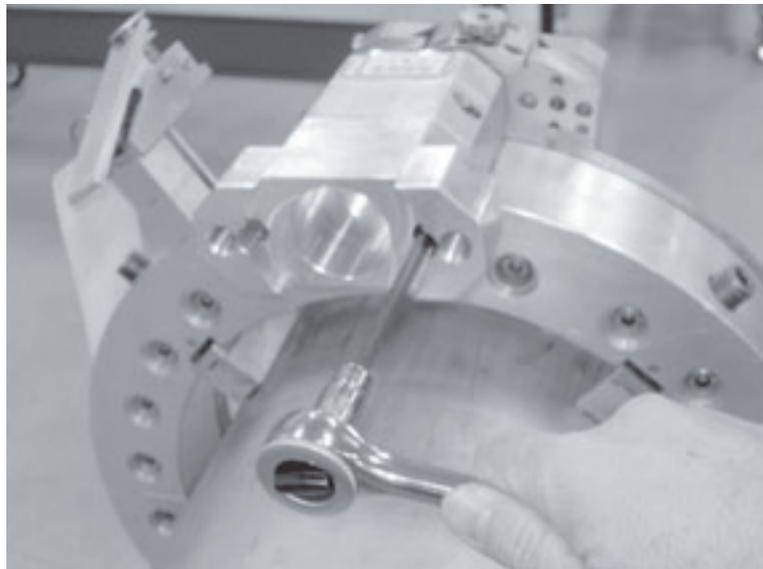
Serrare le 2 viti che fissano l'adattatore del motore idraulico alla sede pignone.
